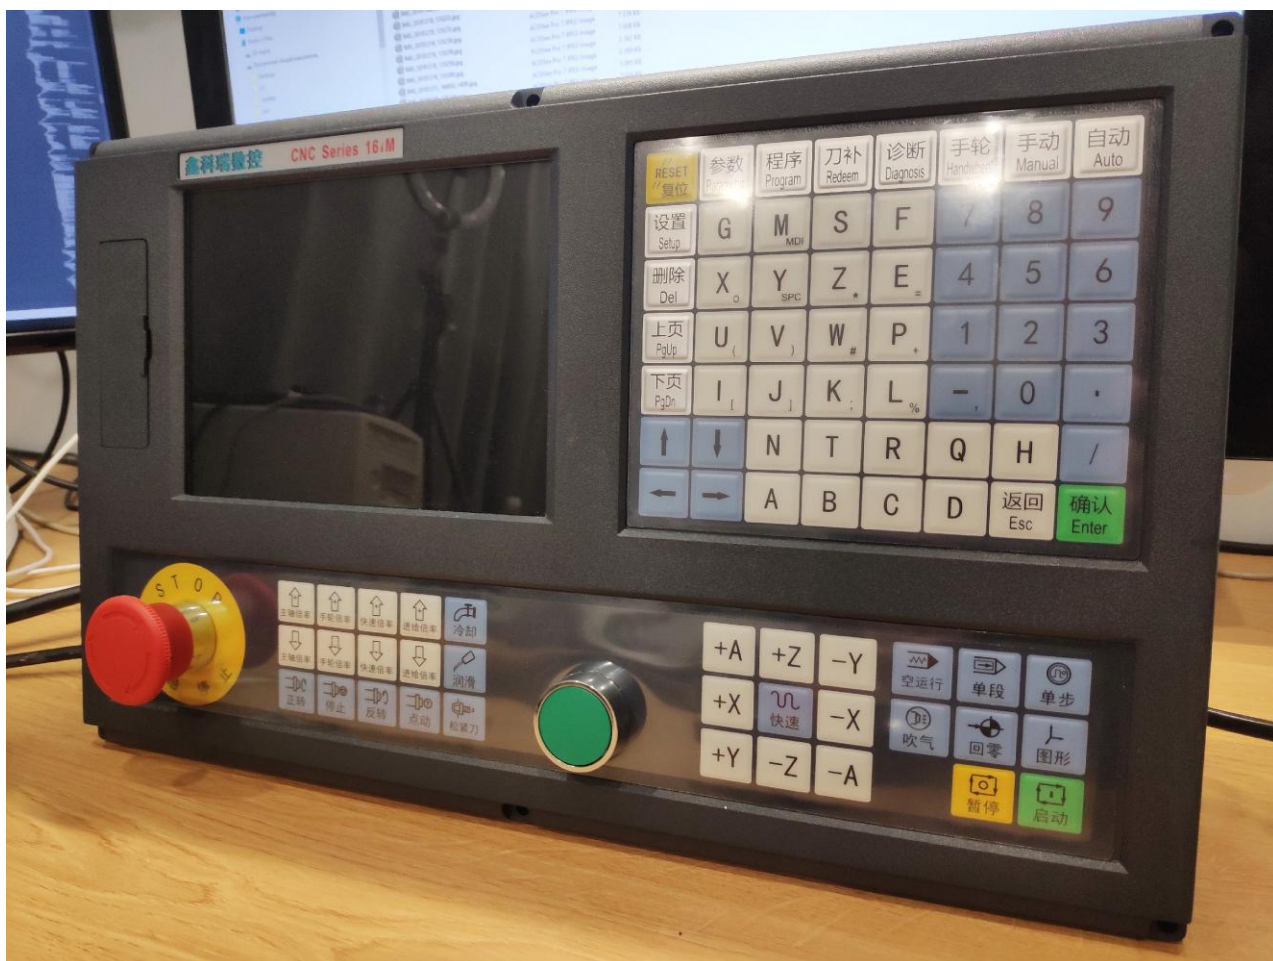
Внешний вид ЧПУ-контроллера NEWKer CNC Series 16iM
